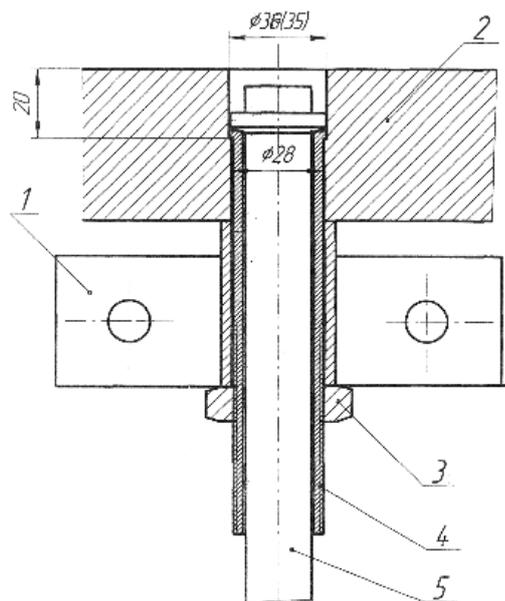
1 – траверса; 2 – крышка люка; 3 – гайка; 4 – установочная втулка; 5 – винт.
